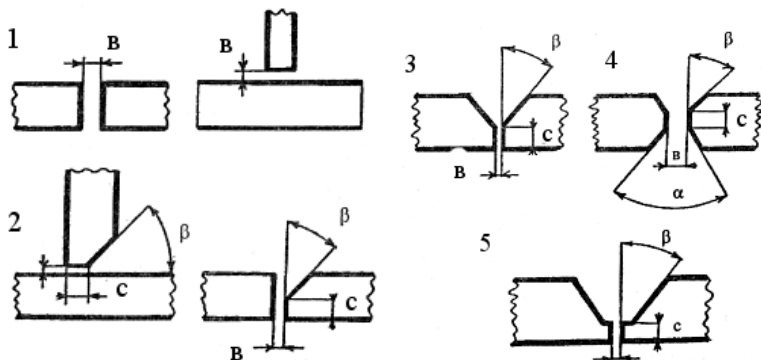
Конструктивные элементы разделки кромок под сварку: в – зазор; с – притупление; β – угол скоса кромок; α – угол разделки кромок; 1 – без разделки кромок; 2 – с разделкой кромок одной детали; 3 – V-образная разделка; 4 – X-образная разделка; 5 – U-образная разделка
